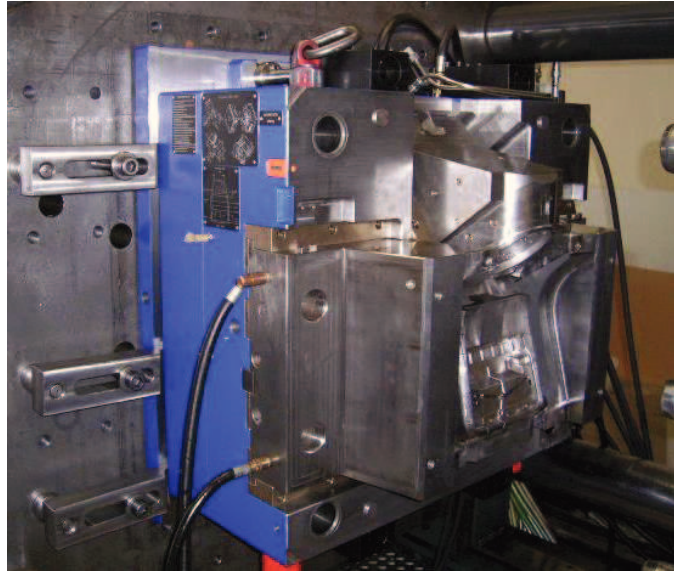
Lado móvel de molde de injeção montado na máquina de injeção
